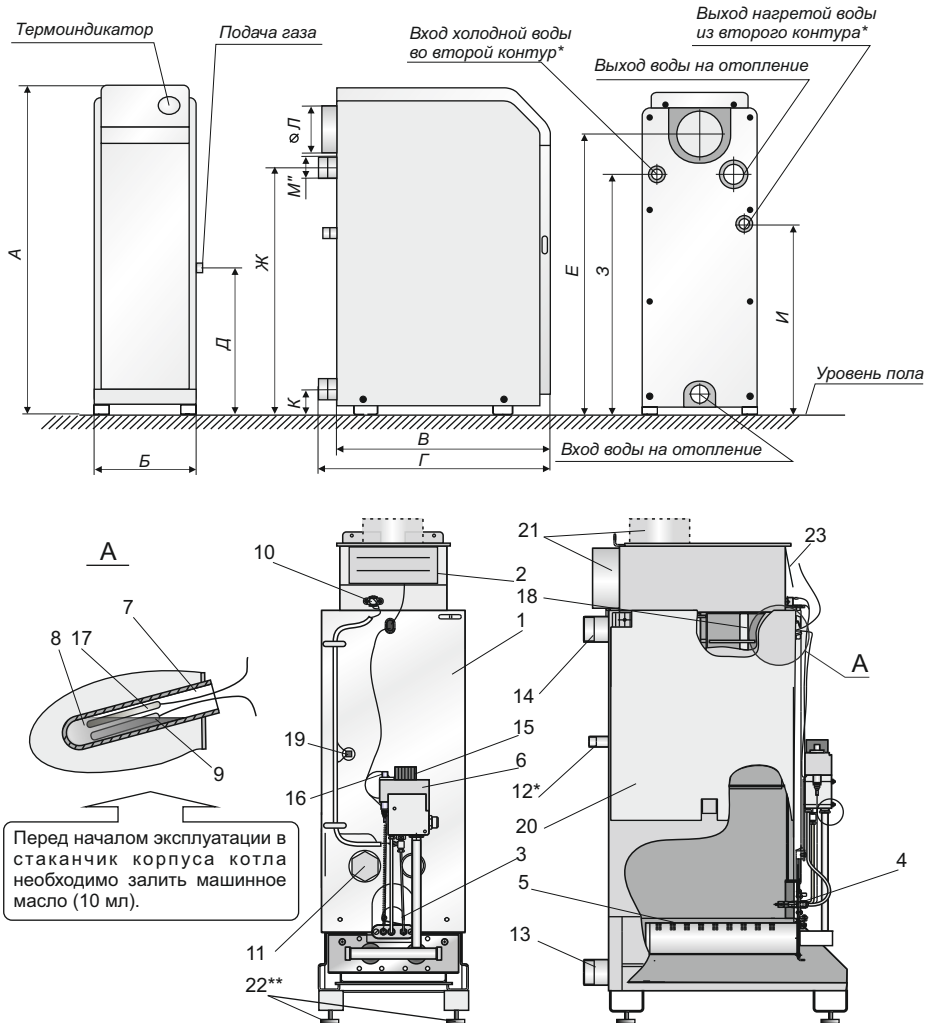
Общий вид и схема конструкции котла "Житомир-3"
